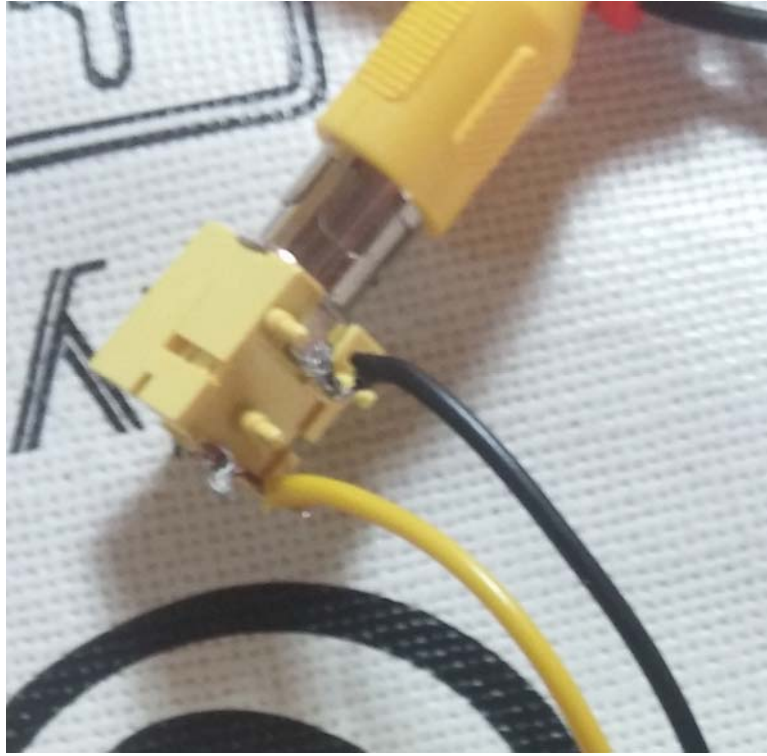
Conector RCA soldado a la placa y con el cable conectado
